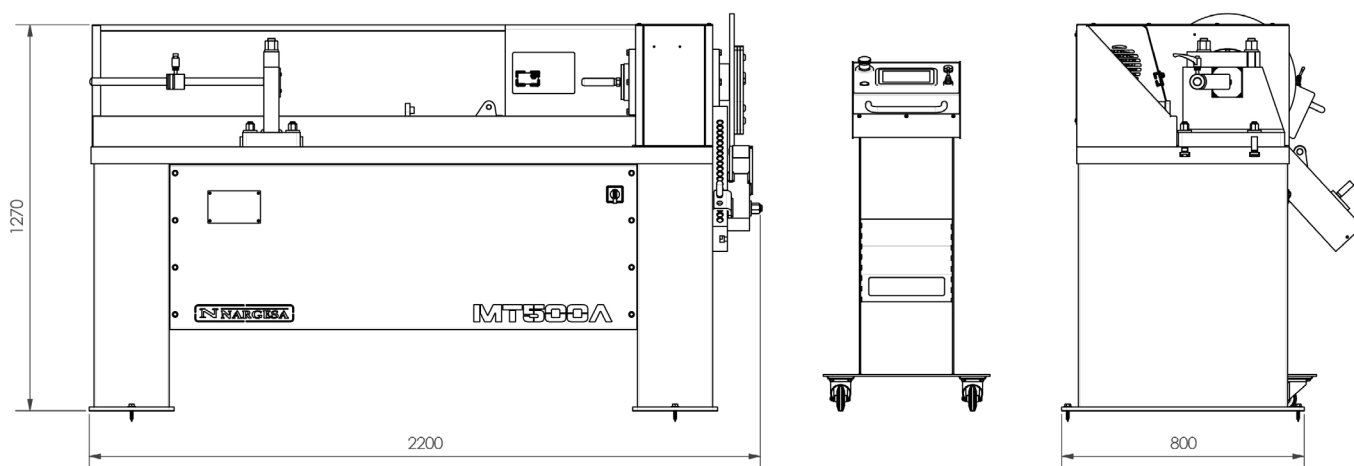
Dimensiones exteriores de la torsionadora MT500A
